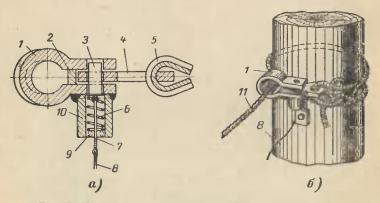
Замок-застежка и крепление им троса на опоре. a— замок-застежка; δ — крепление троса на опоре; I— корпус замка; 2— распорка; 3— палец; 4— подвеска; δ — коуш; δ — пружина; 7— проволочная тяга; δ — шпагат; θ — стальная пробка; 10— патрон; 11— трос.
